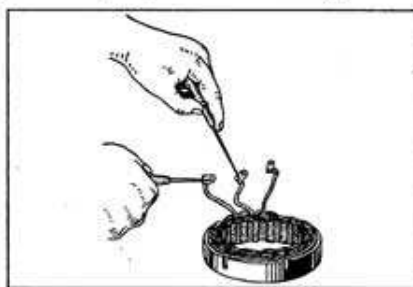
Проверка обмоток статора на обрыв цепи
